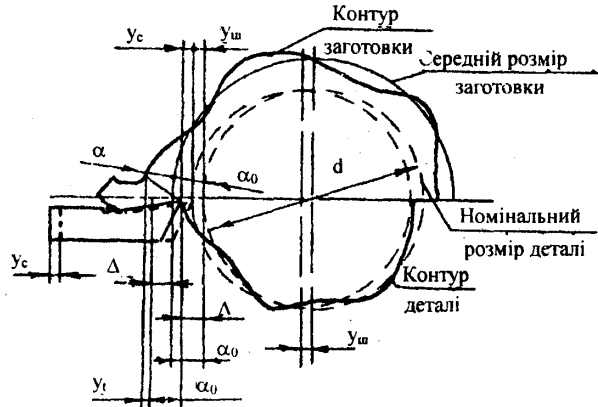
Схема зміни взаємного положення різця та заготовки при коливаннях елементів пружної системи верстата:  $y_{ш}$  – переміщення шпинделя разом із заготовкою;  $y_c$  – переміщення вершини різця внаслідок деформативності супорта;  $\Delta$  – загальна динамічна похибка обробки;  $a_0$  – номінальний діаметр заготовки;  $a$  – відхилення форми заготовки відносно номінального значення;  $y_t$  – зміна припуску в часі
